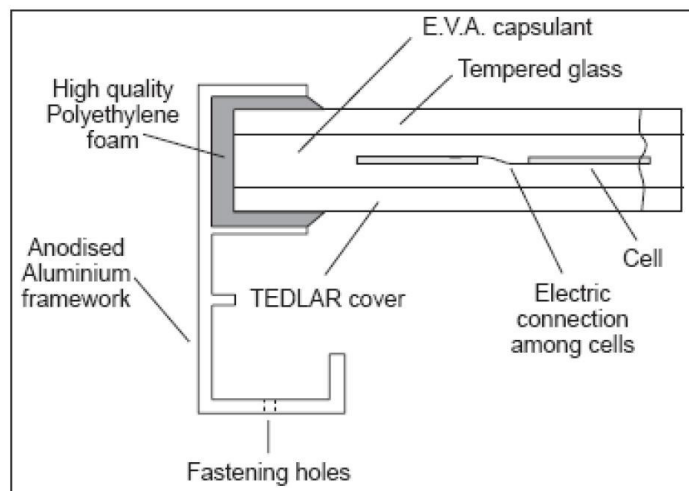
Sezione di un modulo fotovoltaico tipo.
